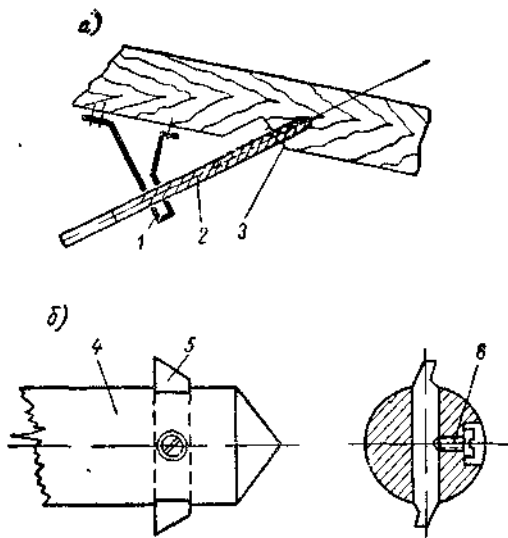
Приспособление для сверления отверстия под дейдвудную трубу: а — кронштейн-кондуктор; б — расточка.
